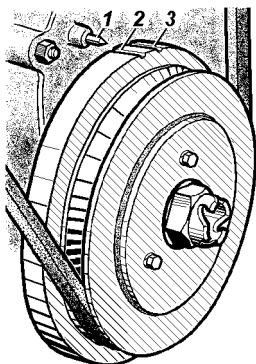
Установочные метки на шкиве-демпфере коленчатого вала двигателей УМЗ:
